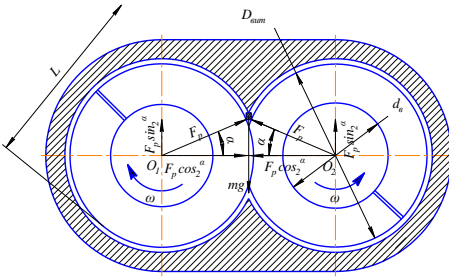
Схема определения геометрических параметров шнеков пресса на поперечном разрезе рабочей камеры пресса:  $D_{\text{вит}}$  – внешний диаметр витка шнека,  $d_b$  – диаметр вала шнека;  $L$  – длина виткового канала шнека;  $O_1, O_2$  – центры валов;  $\omega$  – угловая скорость вала
